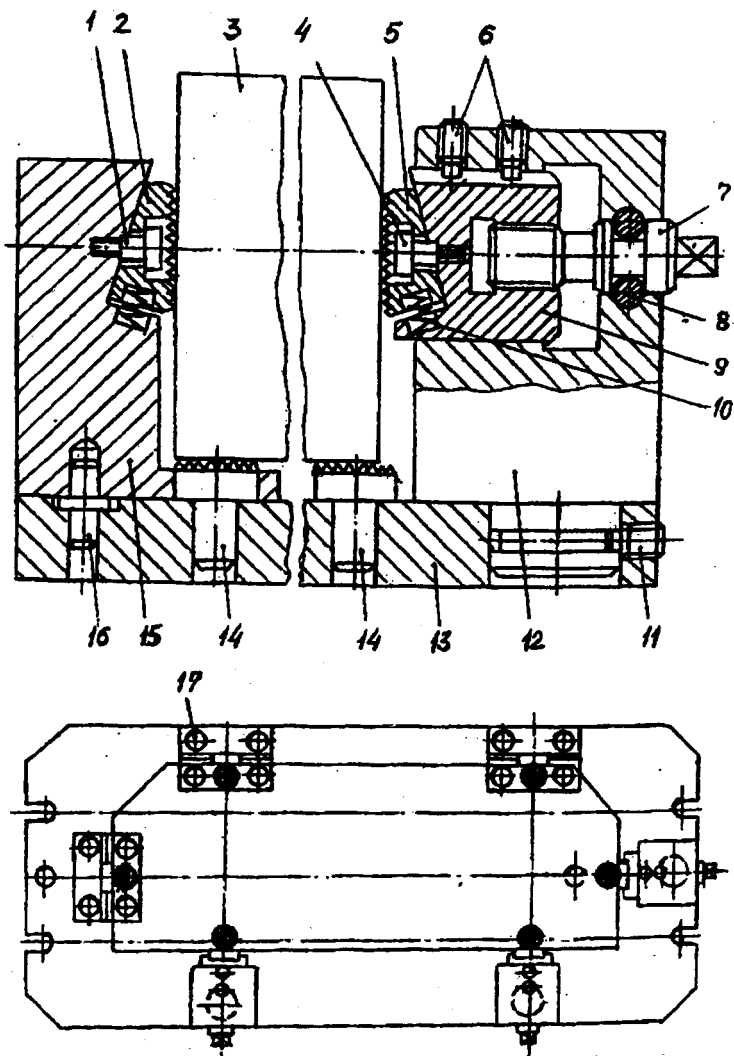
Приспособление для закрепления корпусных заготовок
